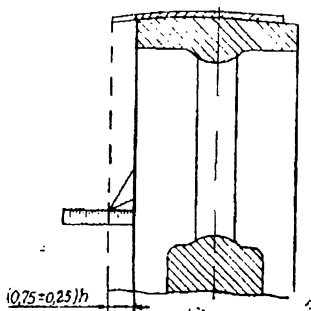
Проверка свеса зубьев ленточной пилы со шкива
